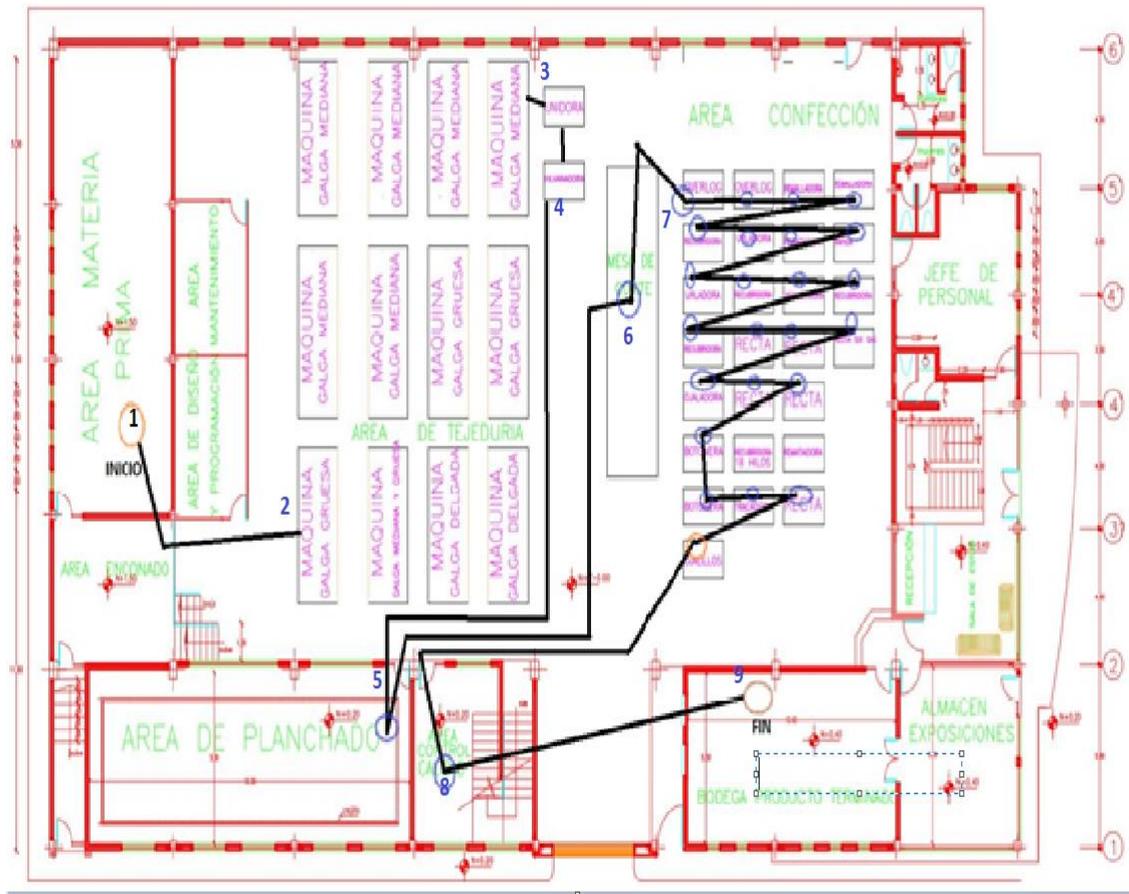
Layout de producción de la planta bajo de la empresa Karmam.
